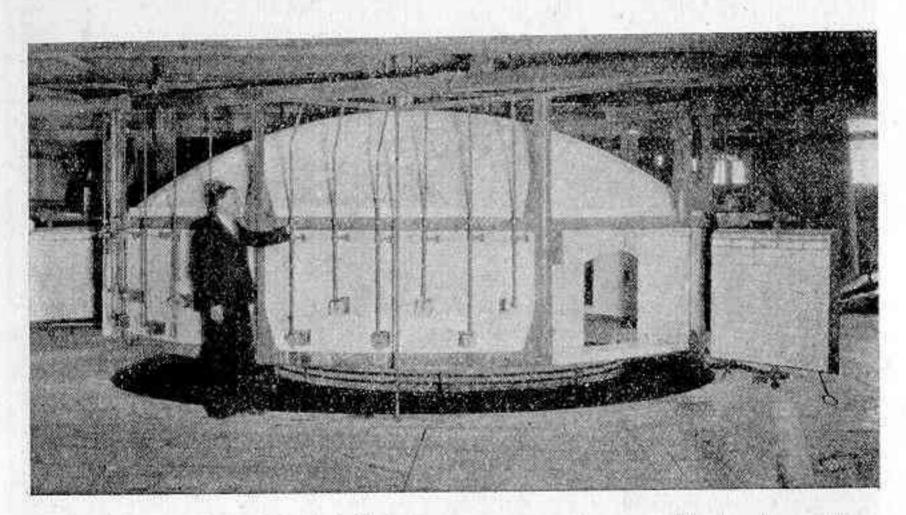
Vista del "iglu", horno para mantener caliente el molde durante la fundición.
